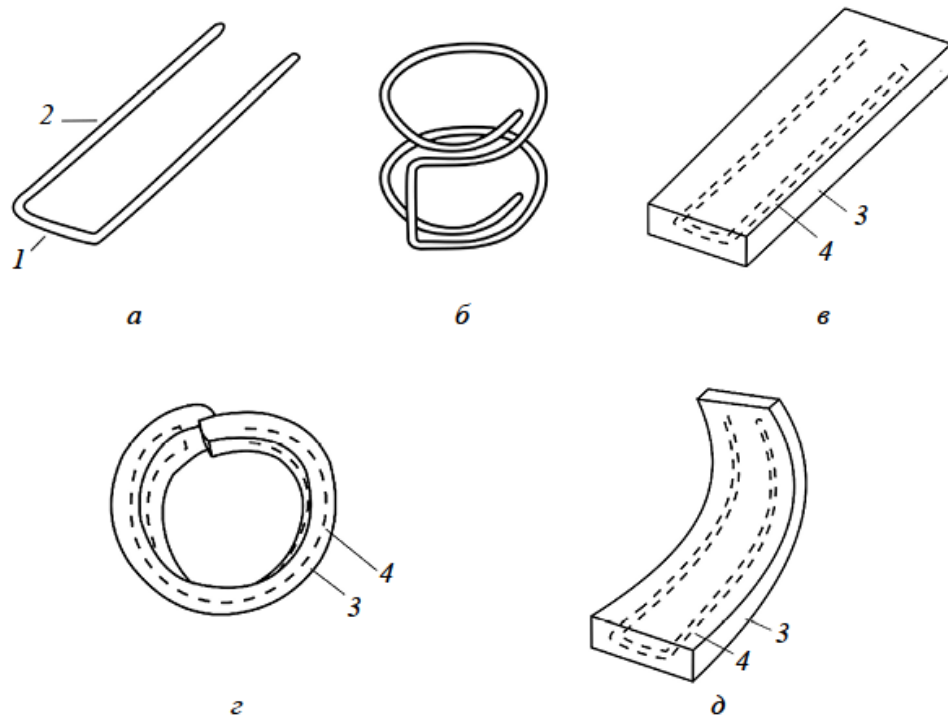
Схема изготовления и формоизменения образца композиционного материала при нагреве и охлаждении: 1, 2 – перемычка и отрезки П-образной проволочной заготовки; 3 – силиконовая матрица, 4 – армирующие элементы из П-образной проволоки.
